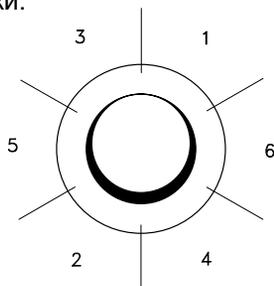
Порядок приварки адаптера к трубе / емкости
